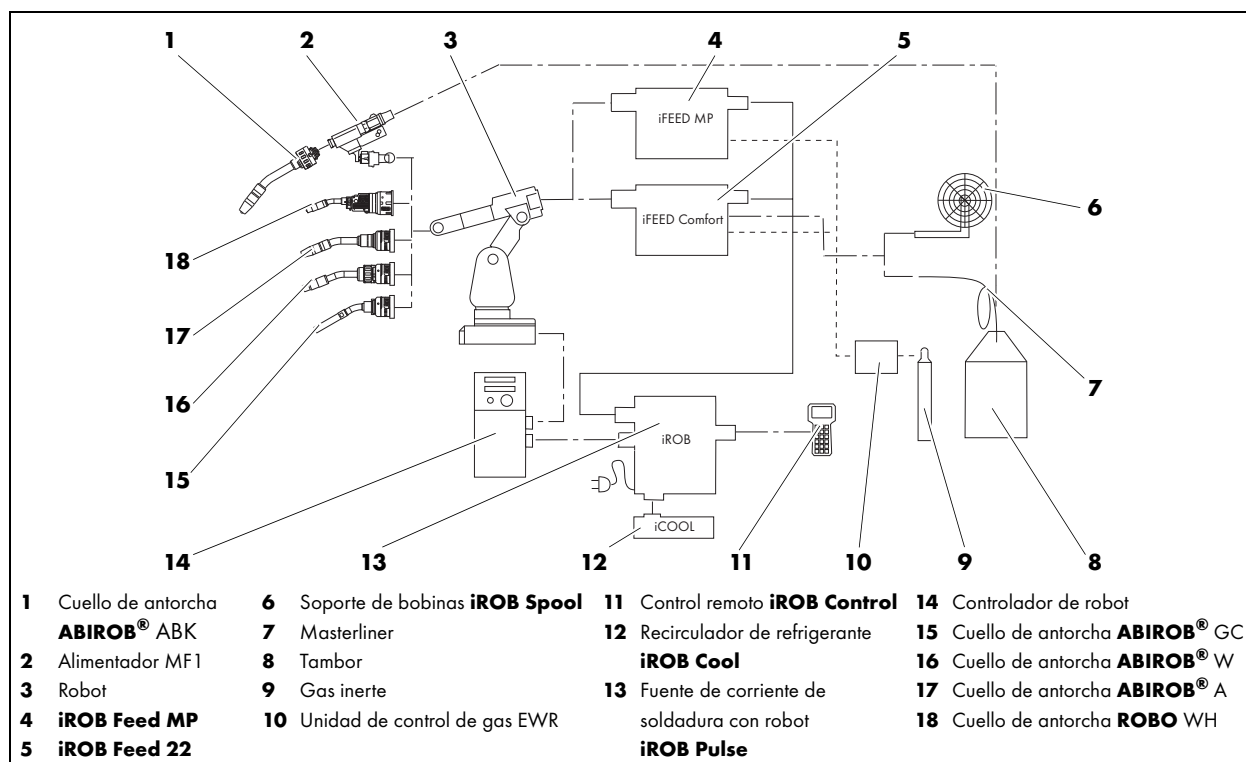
Componentes del equipo de soldadura con robot
